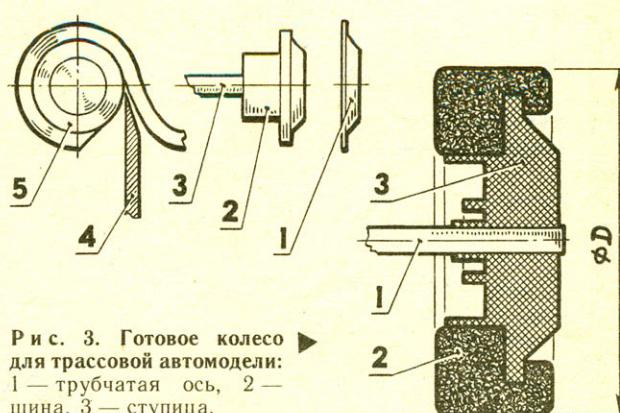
Готовое колесо для трассовой автомодели: 1 — трубчатая ось, 2 — шина, 3 — ступица.
